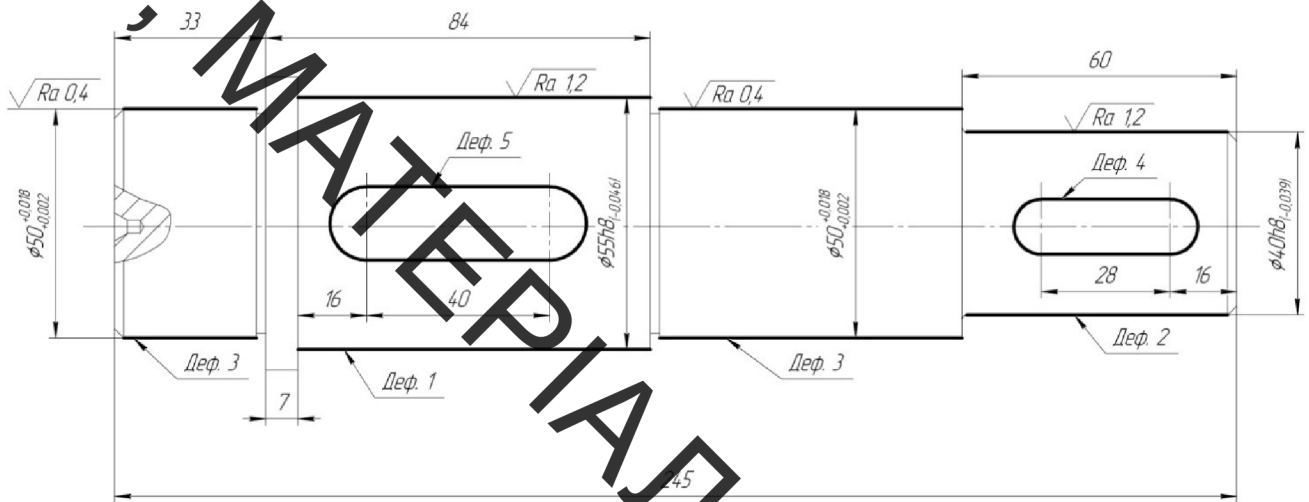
Ремонтне креслення з дефектами поверхонь валу циліндричного редуктора
